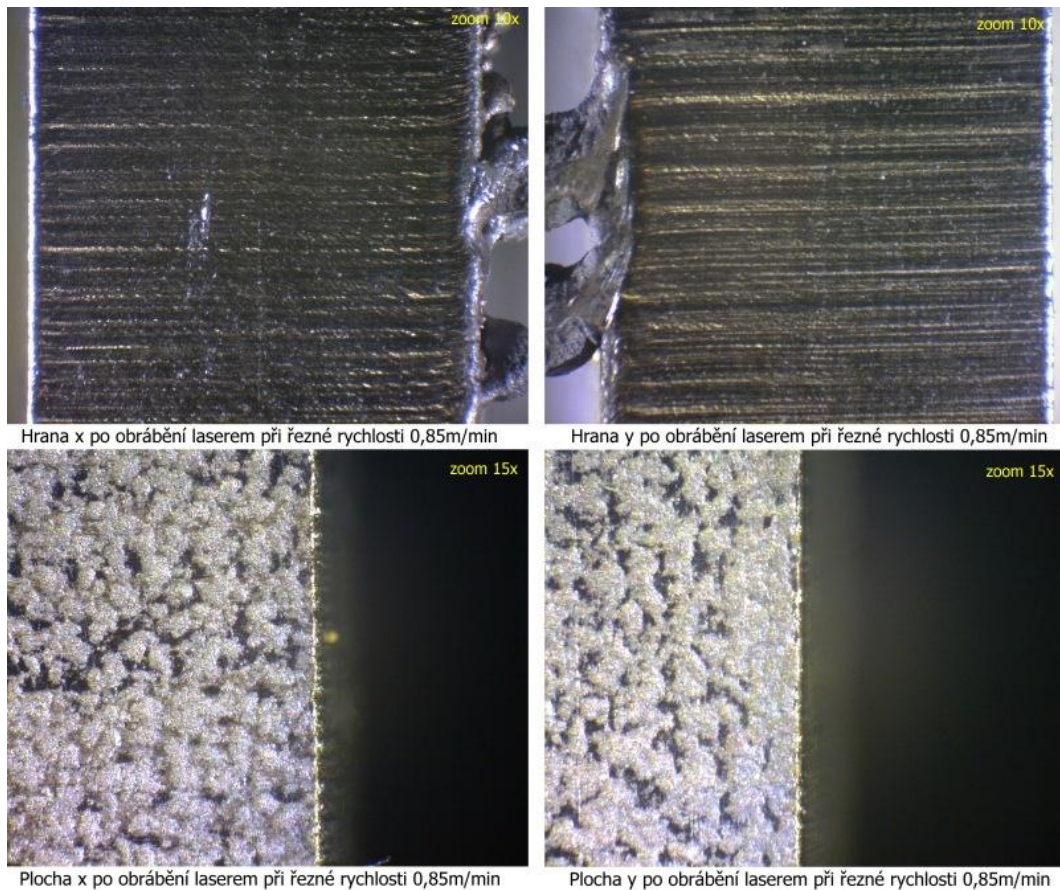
Snímky z mikroskopu vzorku 5 obráběného laserem - materiál 17 349
